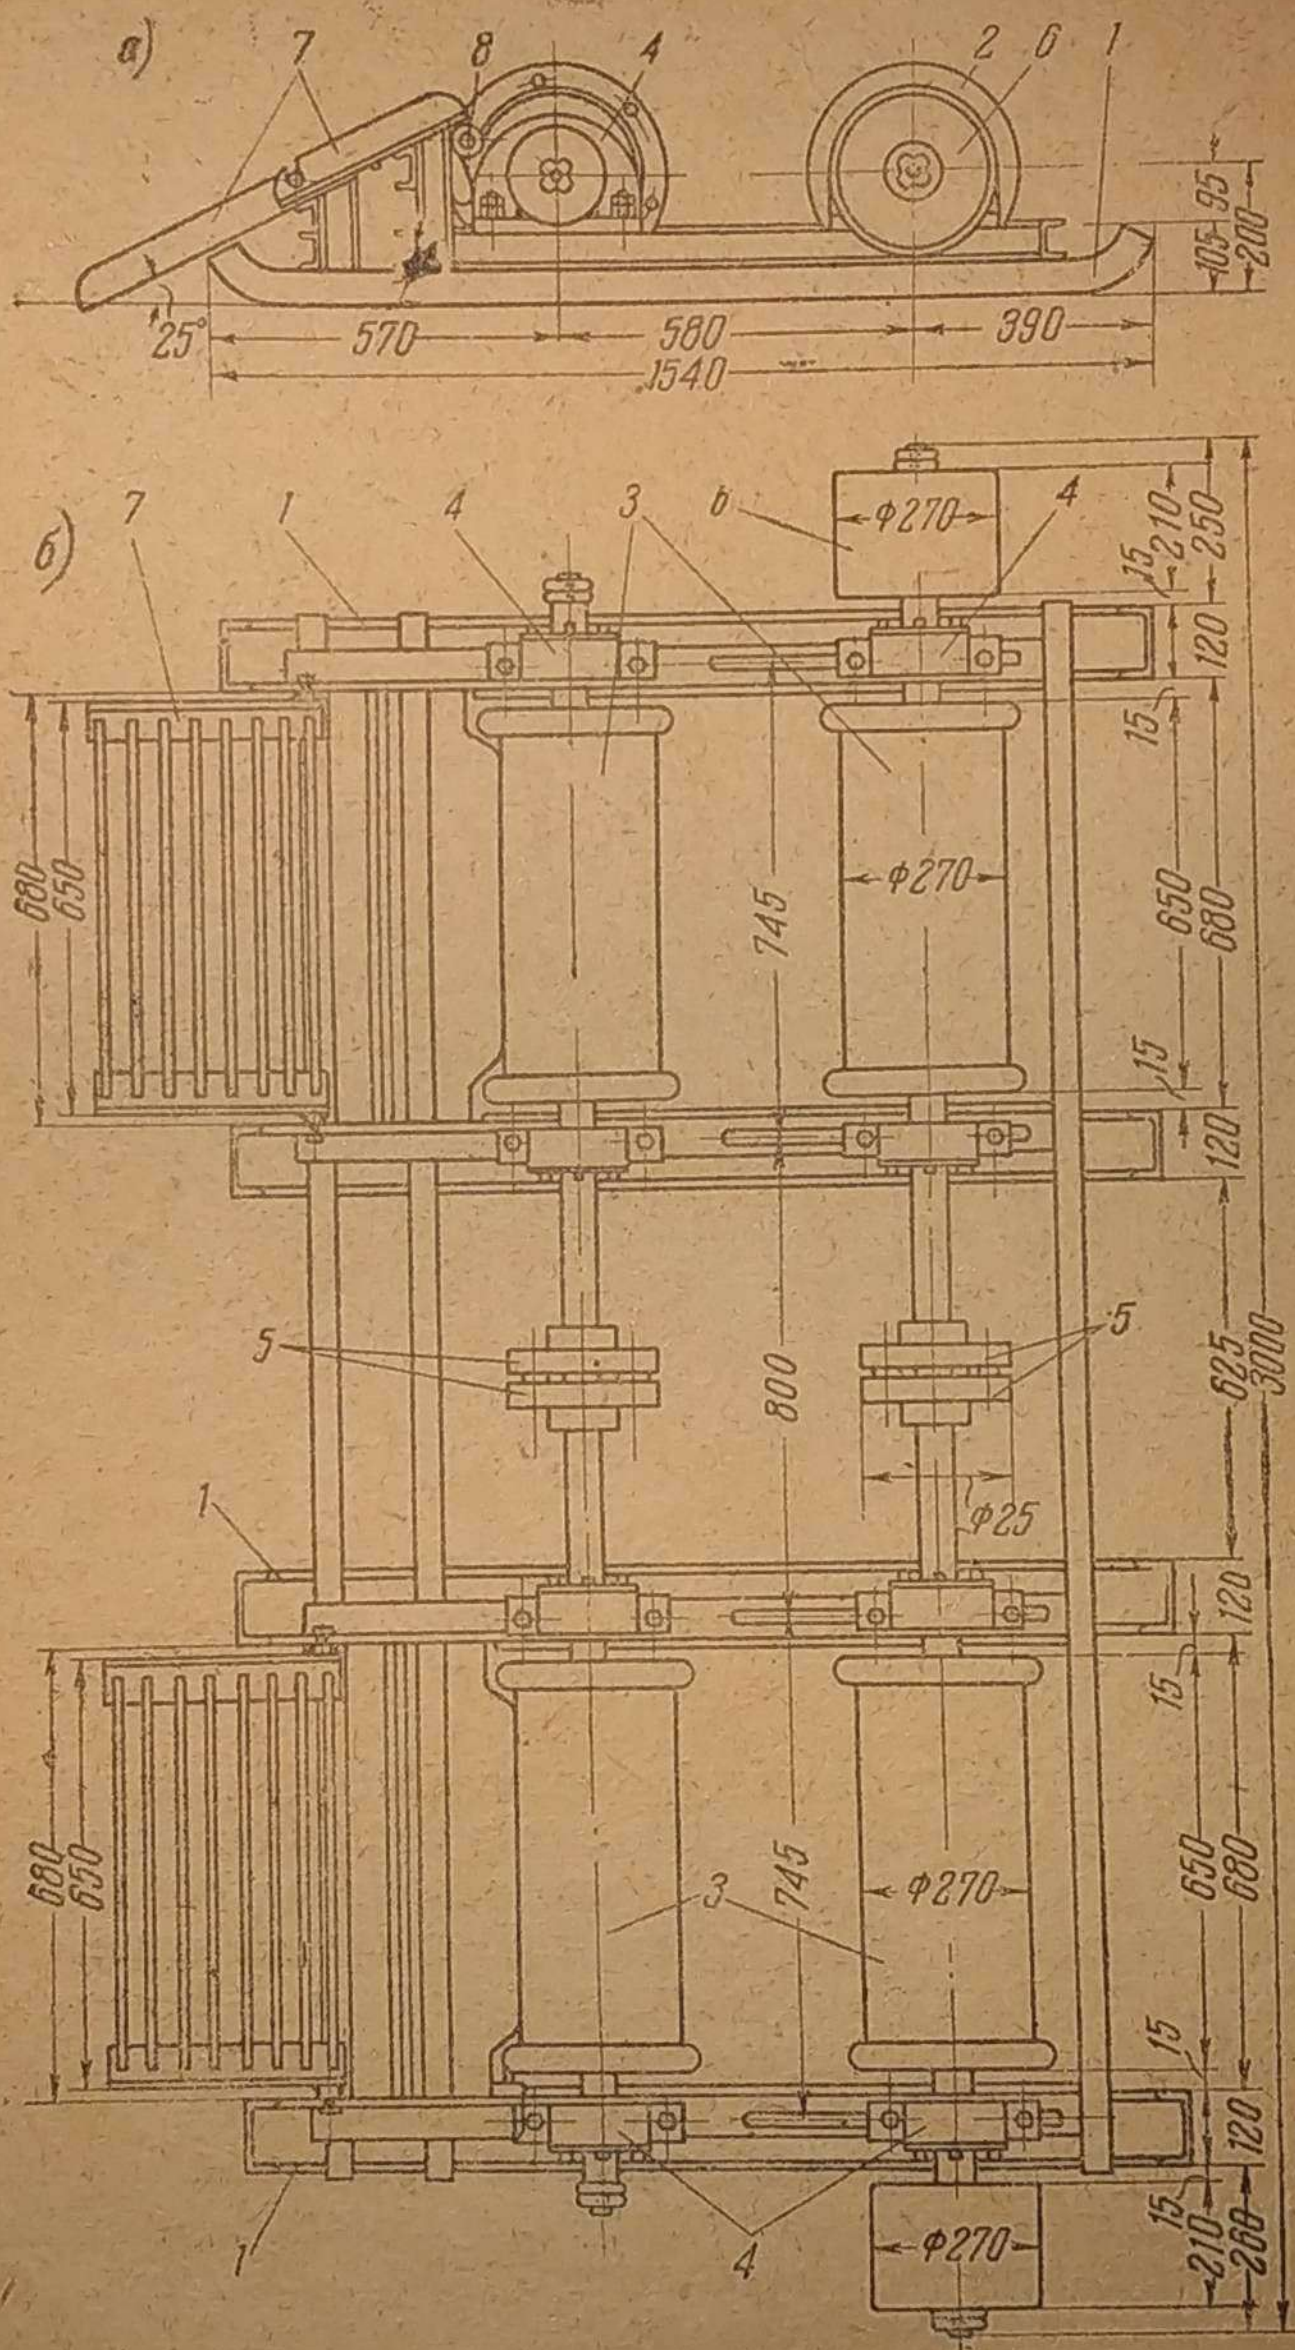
Приспособление для передачи энергии от газогенераторного автомобиля; а — боковой вид; б — план. Обозначения: 1 — рама, 2 — ролик, 3 — вал, 4 — роликподшипник, 5 — полумуфта, 6 — рабочий шкив, 7 — мосток, 8 — стопор
